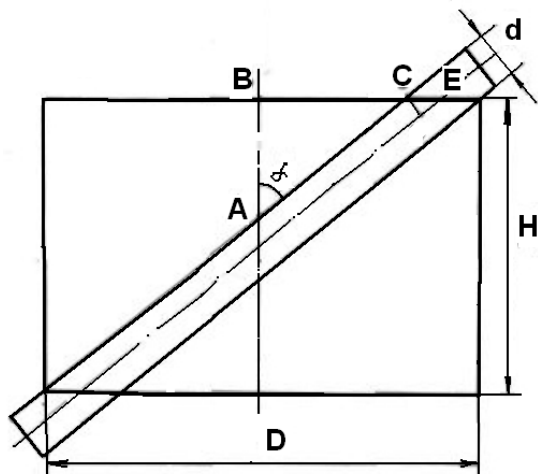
Схема взаимного расположения заготовки и сварочной шины
